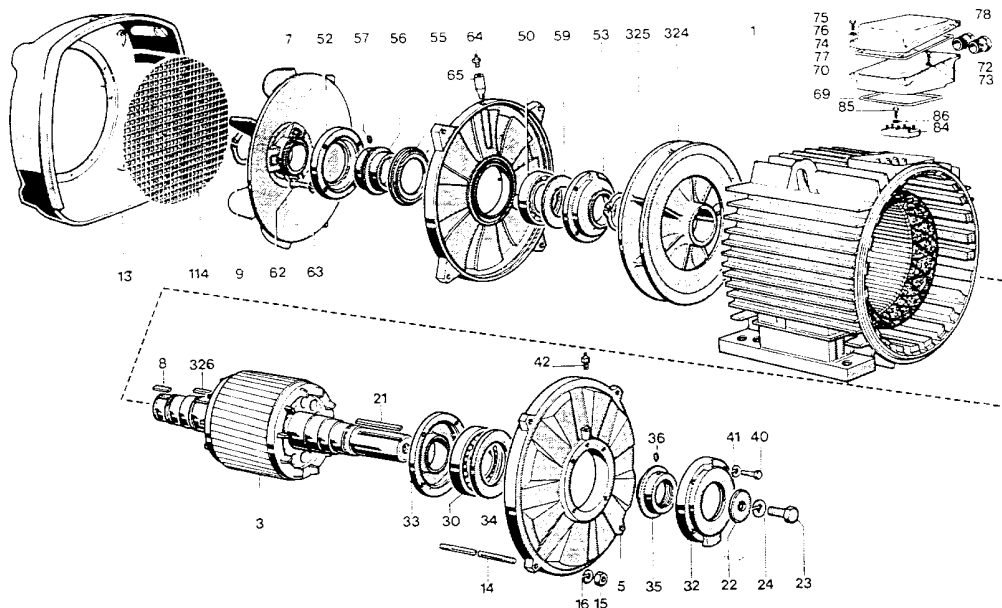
Sprengzeichnung einer Asynchronmaschine
